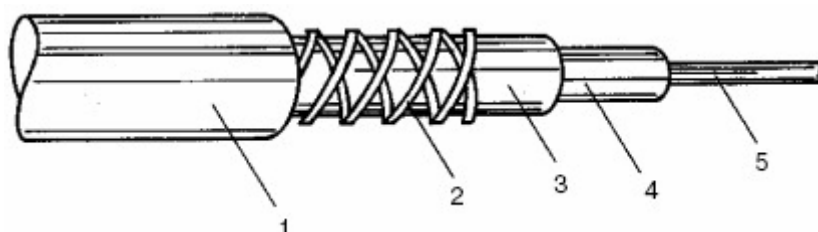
Нагревательный кабель ТЛЭ: 1 – оболочка из ПВХ или полиэтилена; 2 – оплетка из медной проволоки; 3 – пластик; 4 – второй слой изоляции из пластика; 5 – нагревательная жила
